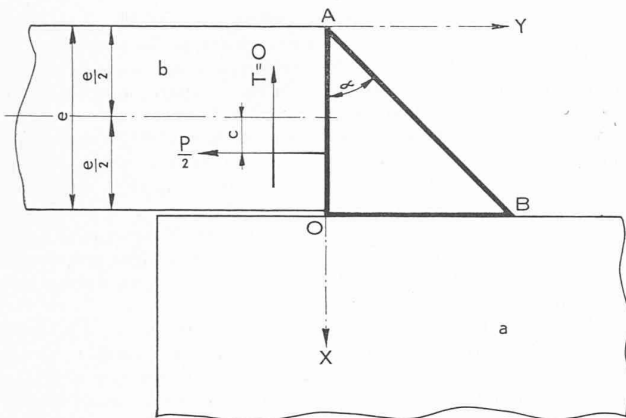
Sollicitation du cordon frontal dans un assemblage soudé par recouvrement.
